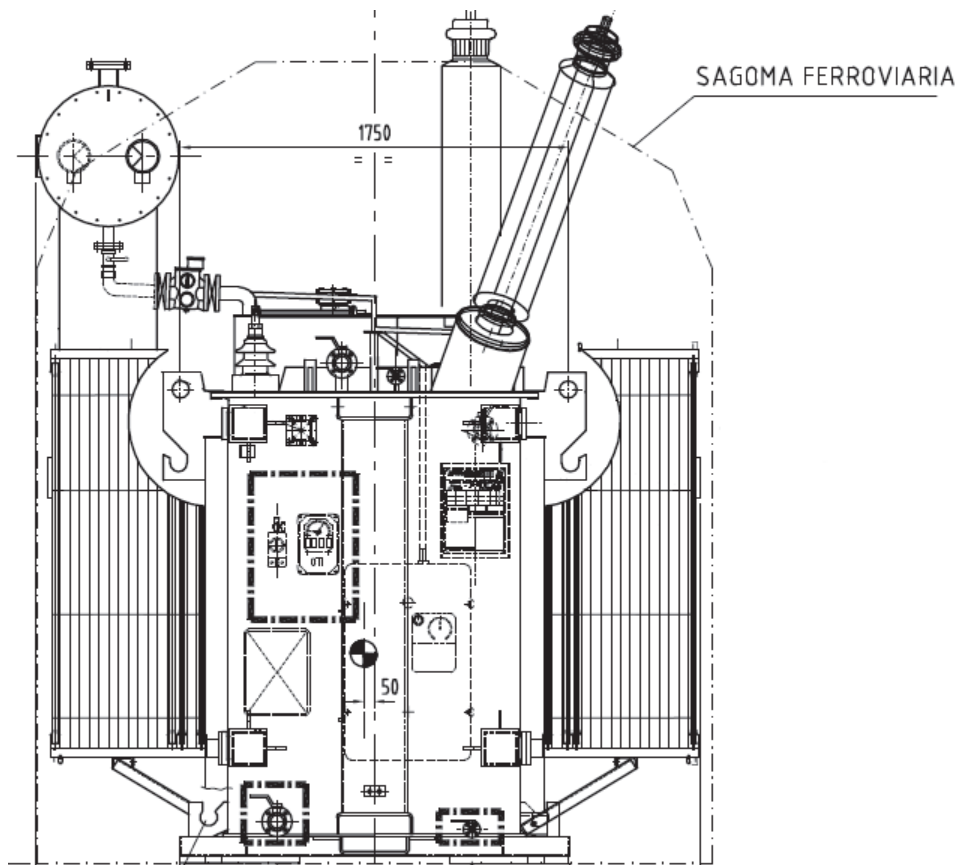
Disegno tecnico del trasformatore di gruppo
